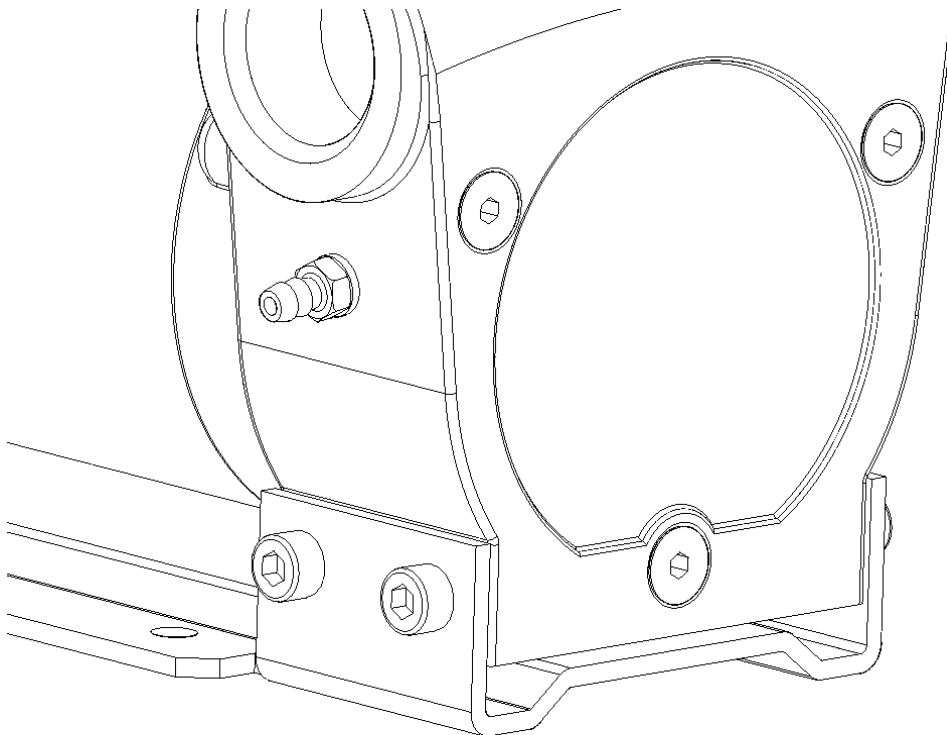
Gewindetülle für Heberschutz eingeschraubt
